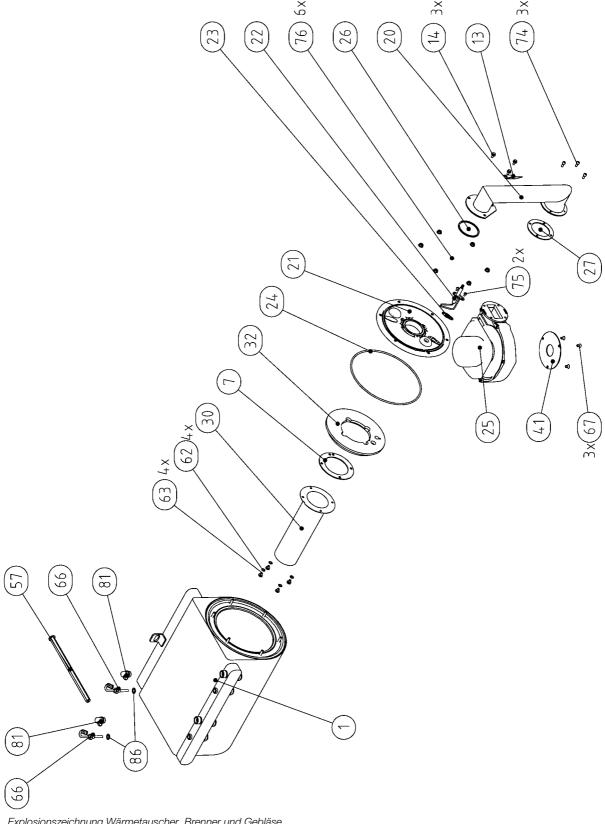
Explosionszeichnung Wärmetauscher, Brenner und Gebläse
